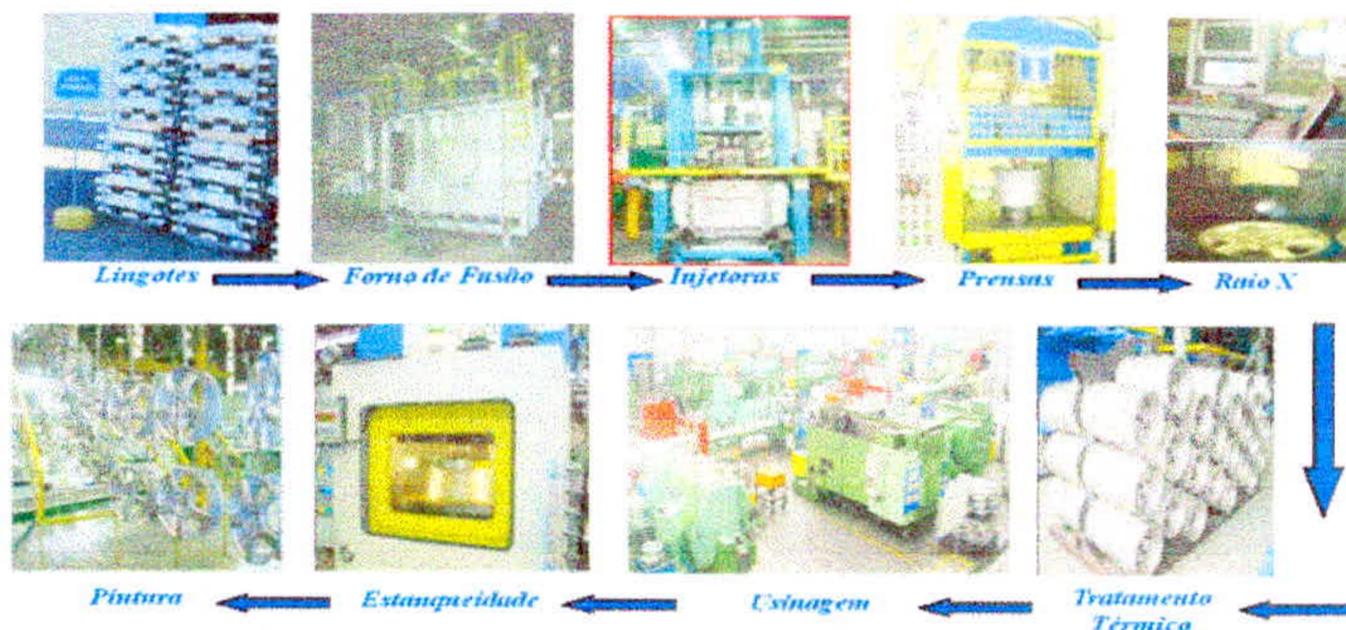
Fluxo de Processo de Fabricação de Roda de Alumínio
